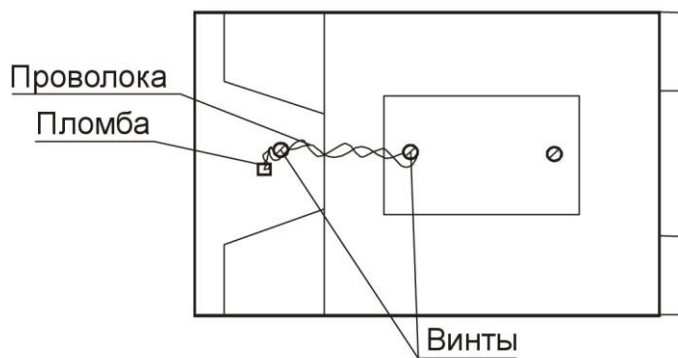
Схема пломбировки вторичного преобразователя при креплении на DIN-рейку
